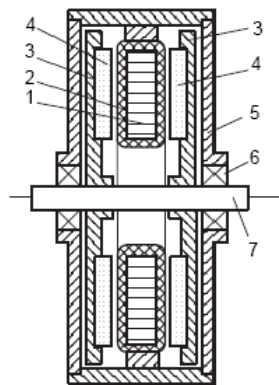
Descriptif de la machine à flux axial stator interne [16].
